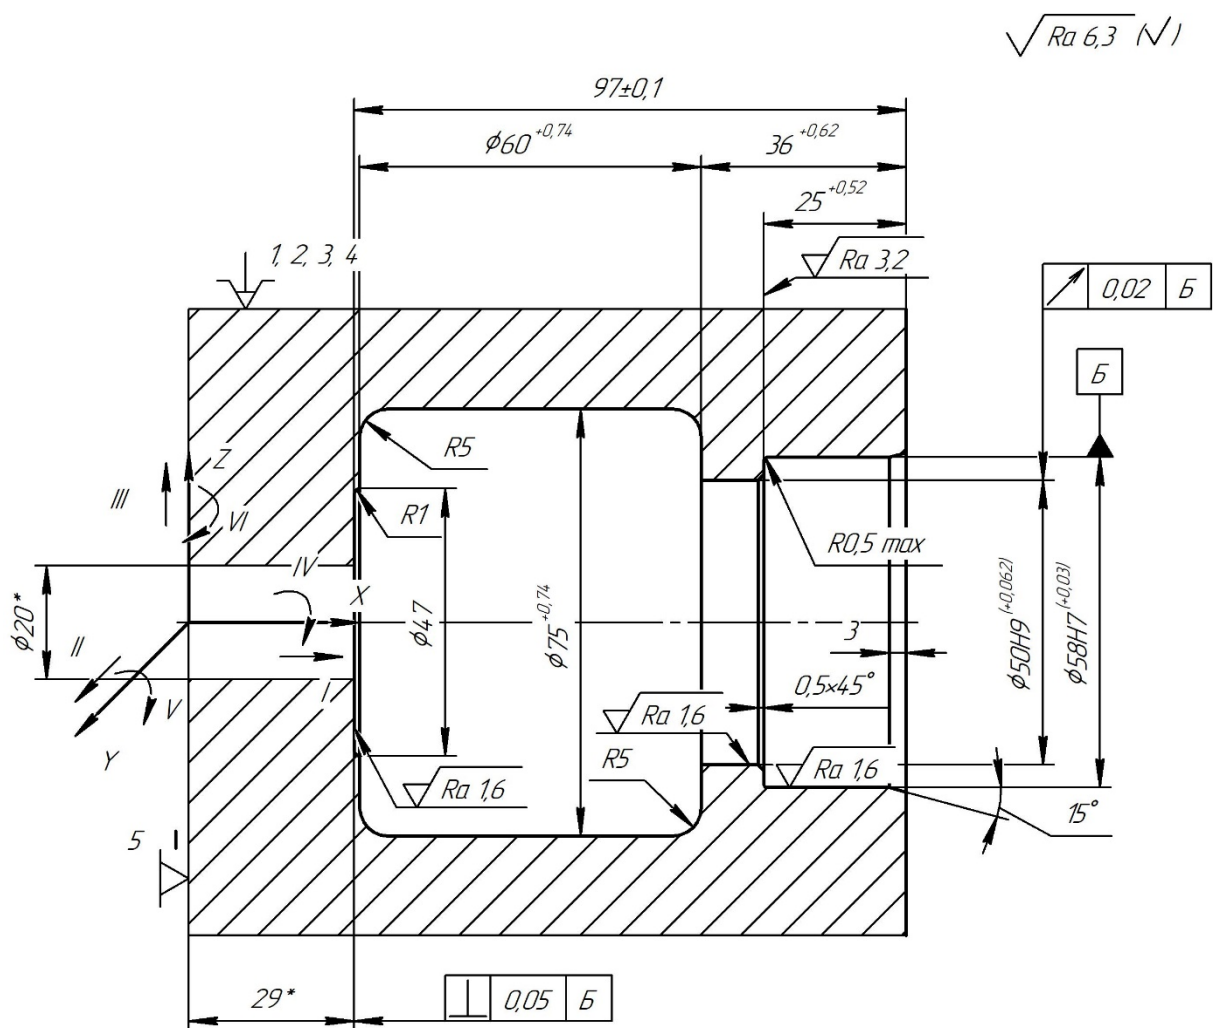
Схема базування й закріплення заготовки на операції 030 токарно-гвинторізній
